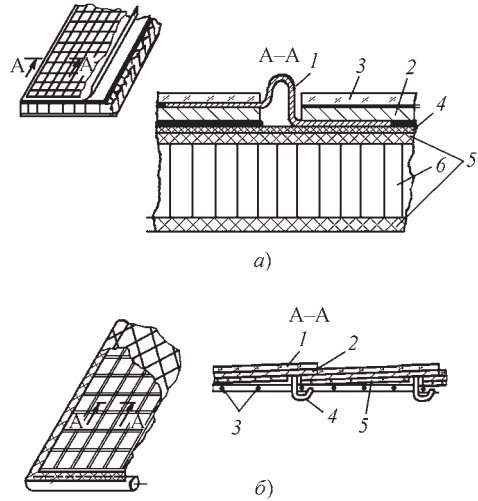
Схемы конструкции солнечной батареи: а — жесткой: 1 — коммутационная шина; 2 — ФЭП; 3 — защитное стекло; 4 — изоляционная пленка; 5 — верхняя и нижняя облицовка сотовой конструкции; 6 — алюминиевый наполнитель сотовой конструкции; б — полужесткой: 1 — лицевое защитное стекло; 2 — ФЭП; 3 — сетчатая подложка; 4 — элемент крепления; 5 — тыльное защитное стекло
